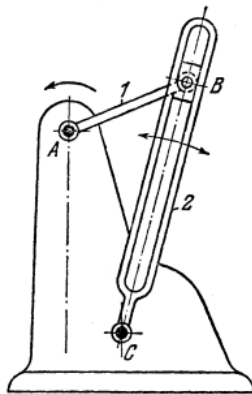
Четырёхзвенный кулисный механизм с качающейся кулисой
